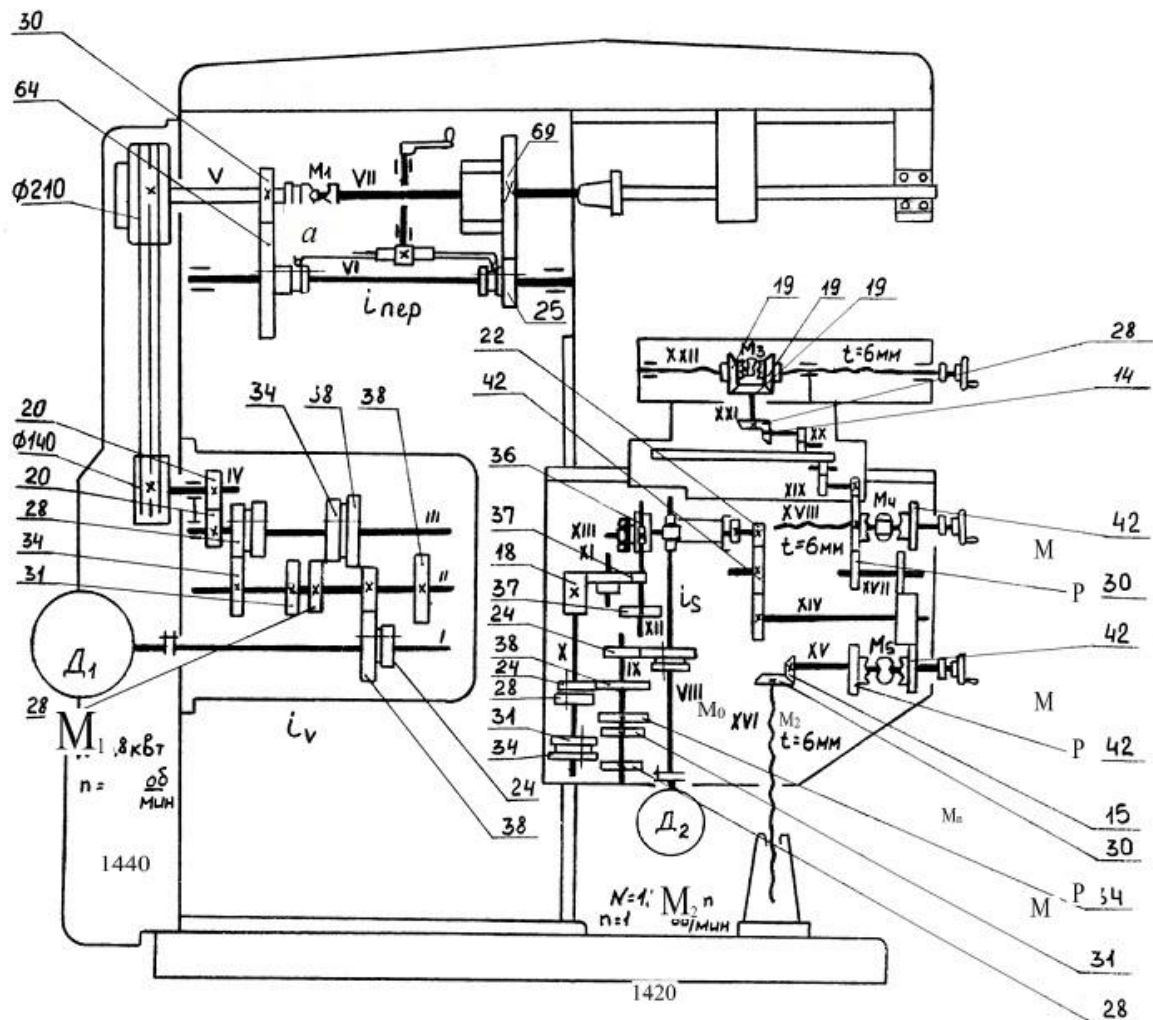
Кинематическая схема универсально-фрезерного станка 6N81
